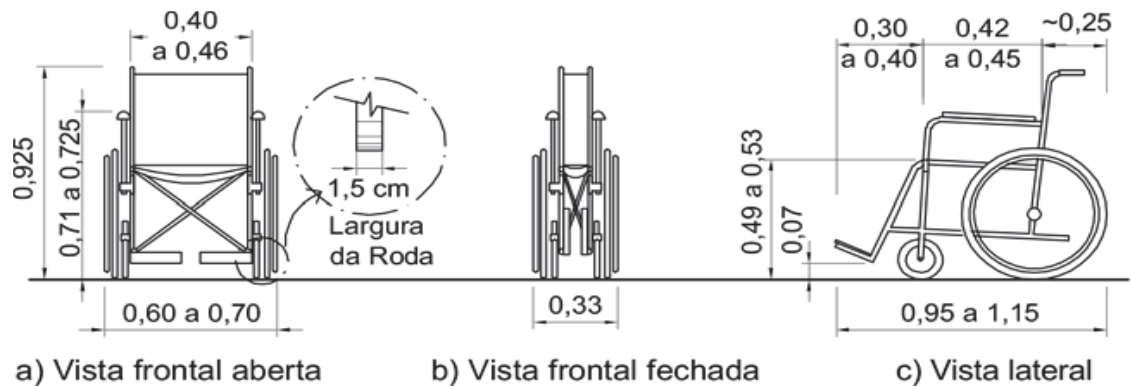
Dimensões limitantes para a construção de cadeira de rodas
